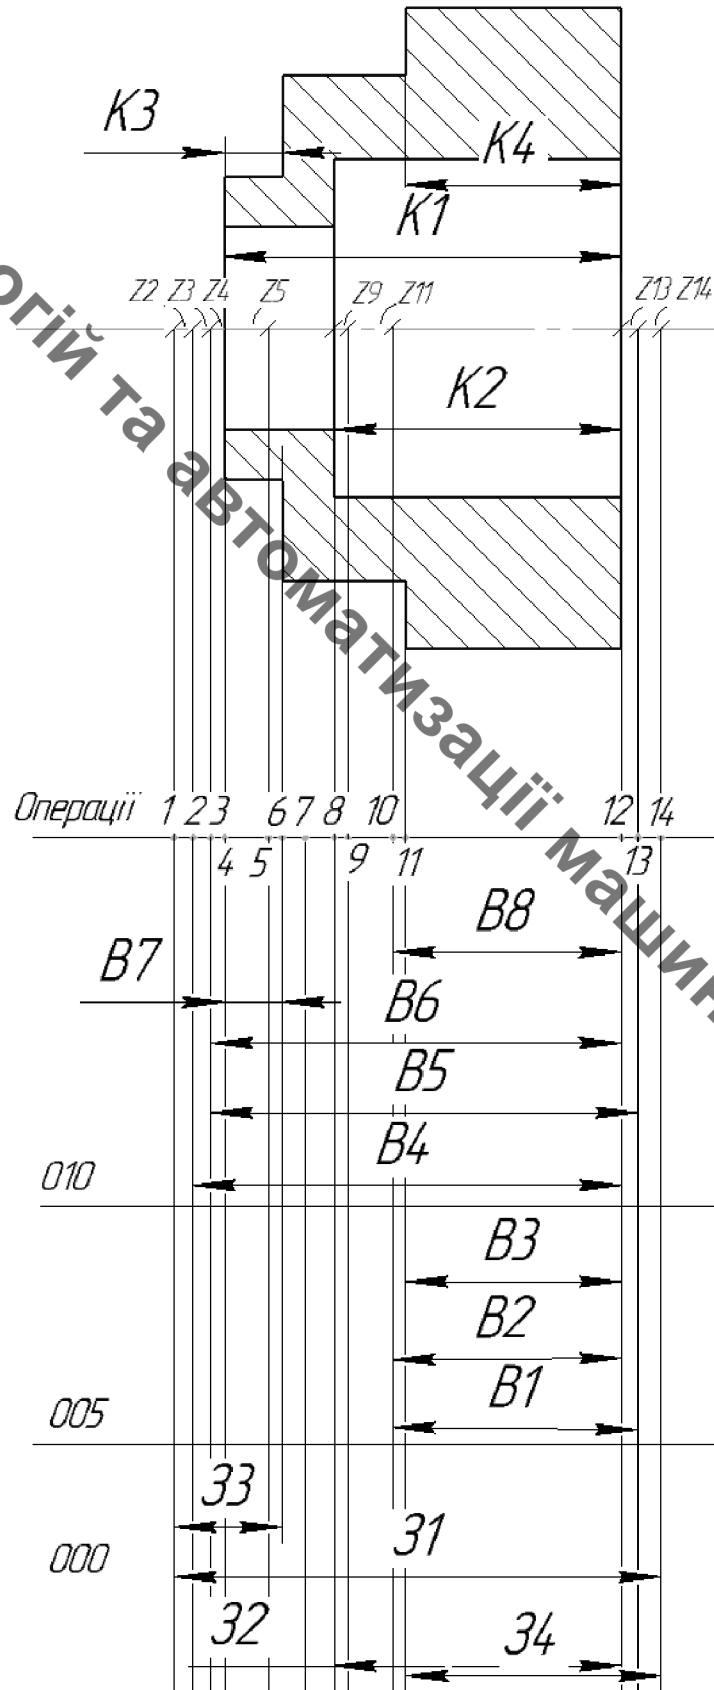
Розмірна схема деталі «Корпус клапана Г.36.004»
